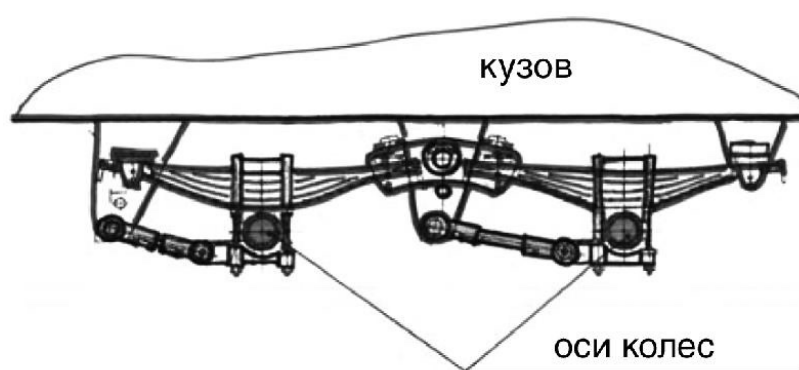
Схема двухосной тележки полуприцепа с рессорно-балансирной подвеской
